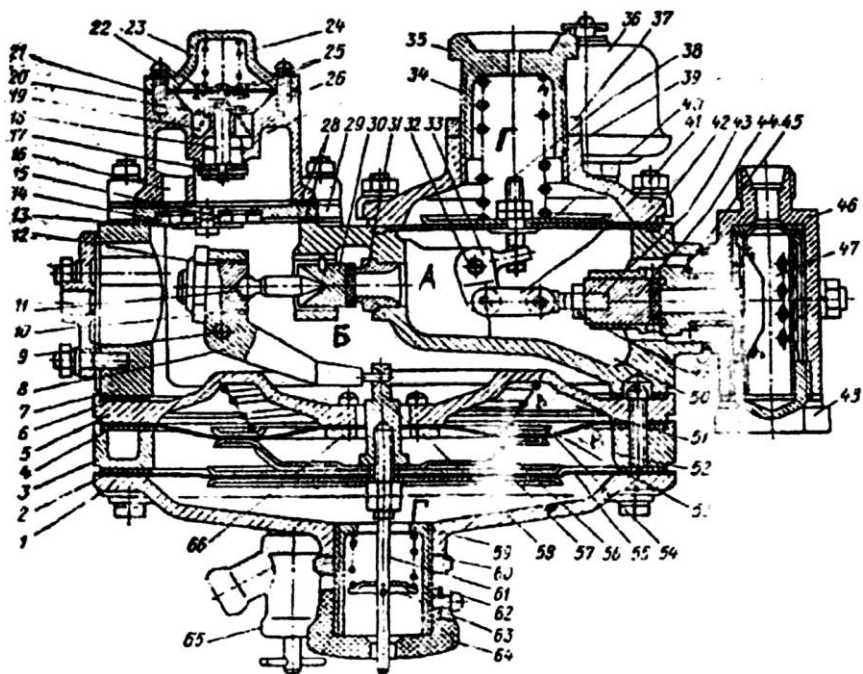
Двухступенчатый редуктор диафрагменно-рычажного типа
